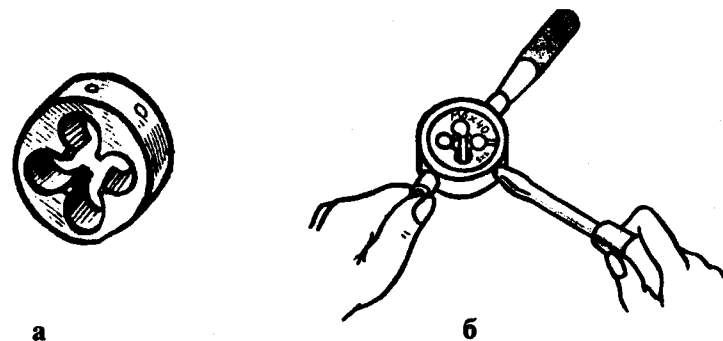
Круглая плашка (а) и ее закрепление в плашкодержателе (б)
